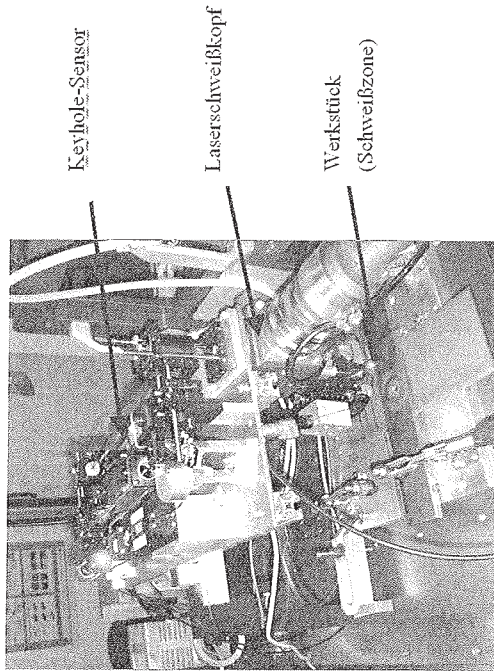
Keyhole-Sensor am Bearbeitungskopf einer Laserschweißanlage.
